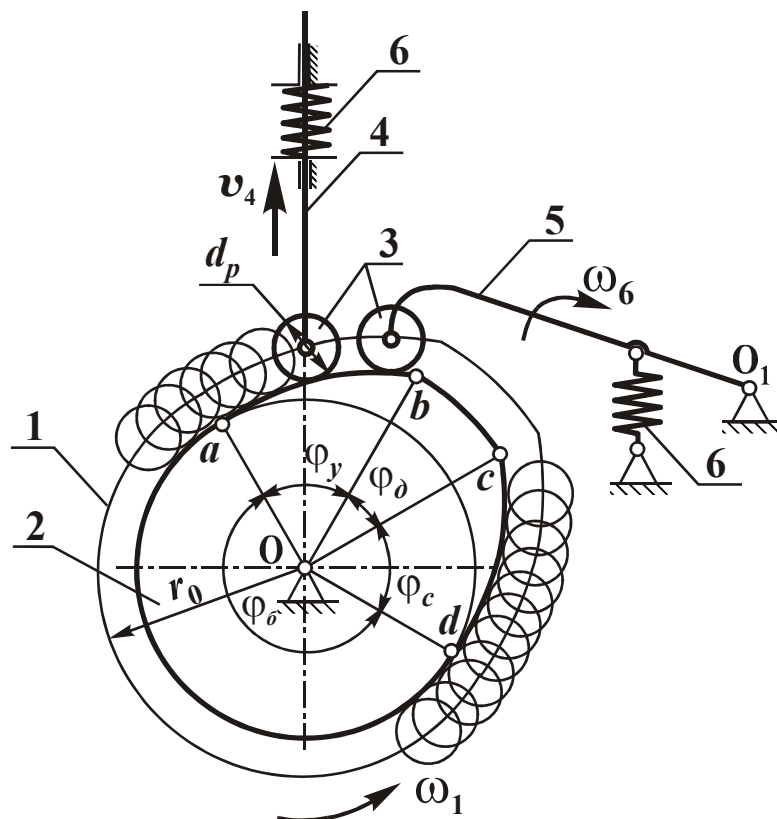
Схема кулачкового механизма с вращательным и поступательно движущимся звеном
